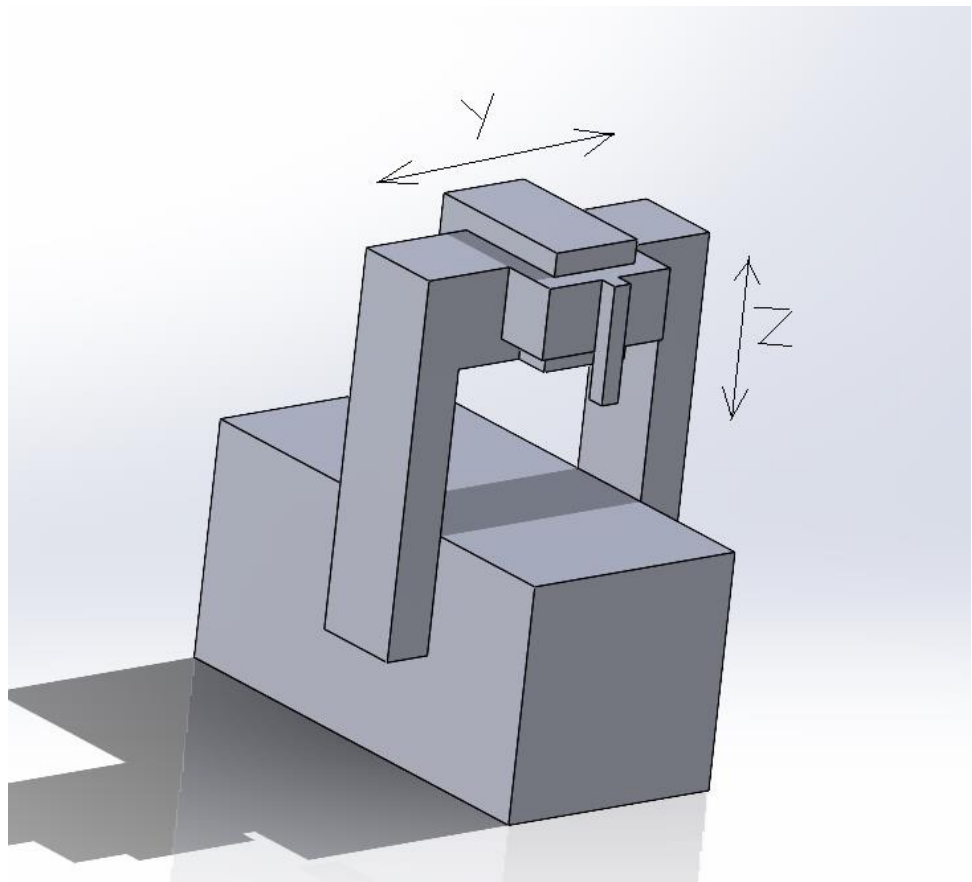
Компоновка де рухається заготовка відносно нерухомого плазморіза
